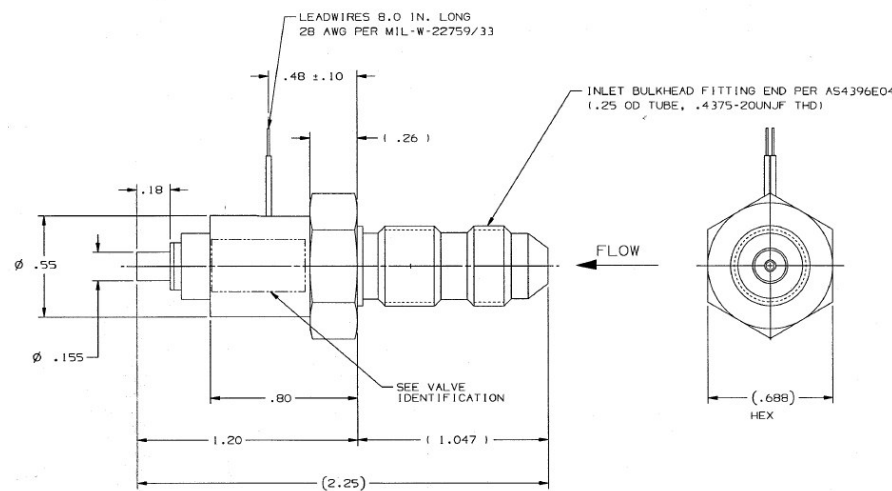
Technische Zeichnung der Lagethruster
